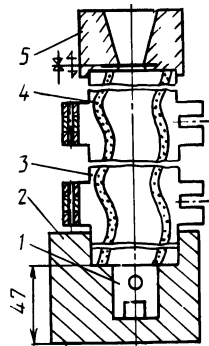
Литейная форма для отливки роторов винтовых насосов
